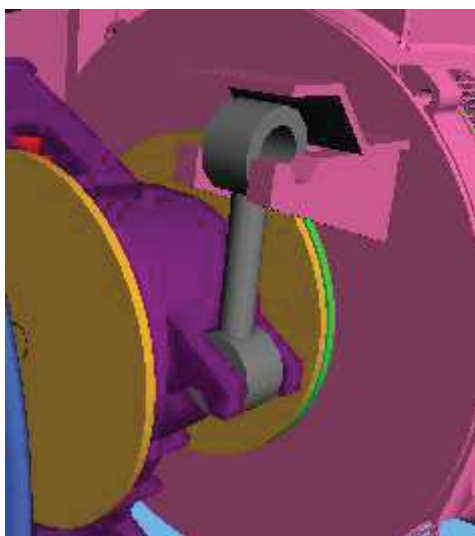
Kompletní MBS model částečně odpruženého pohonu – přední pohled.
